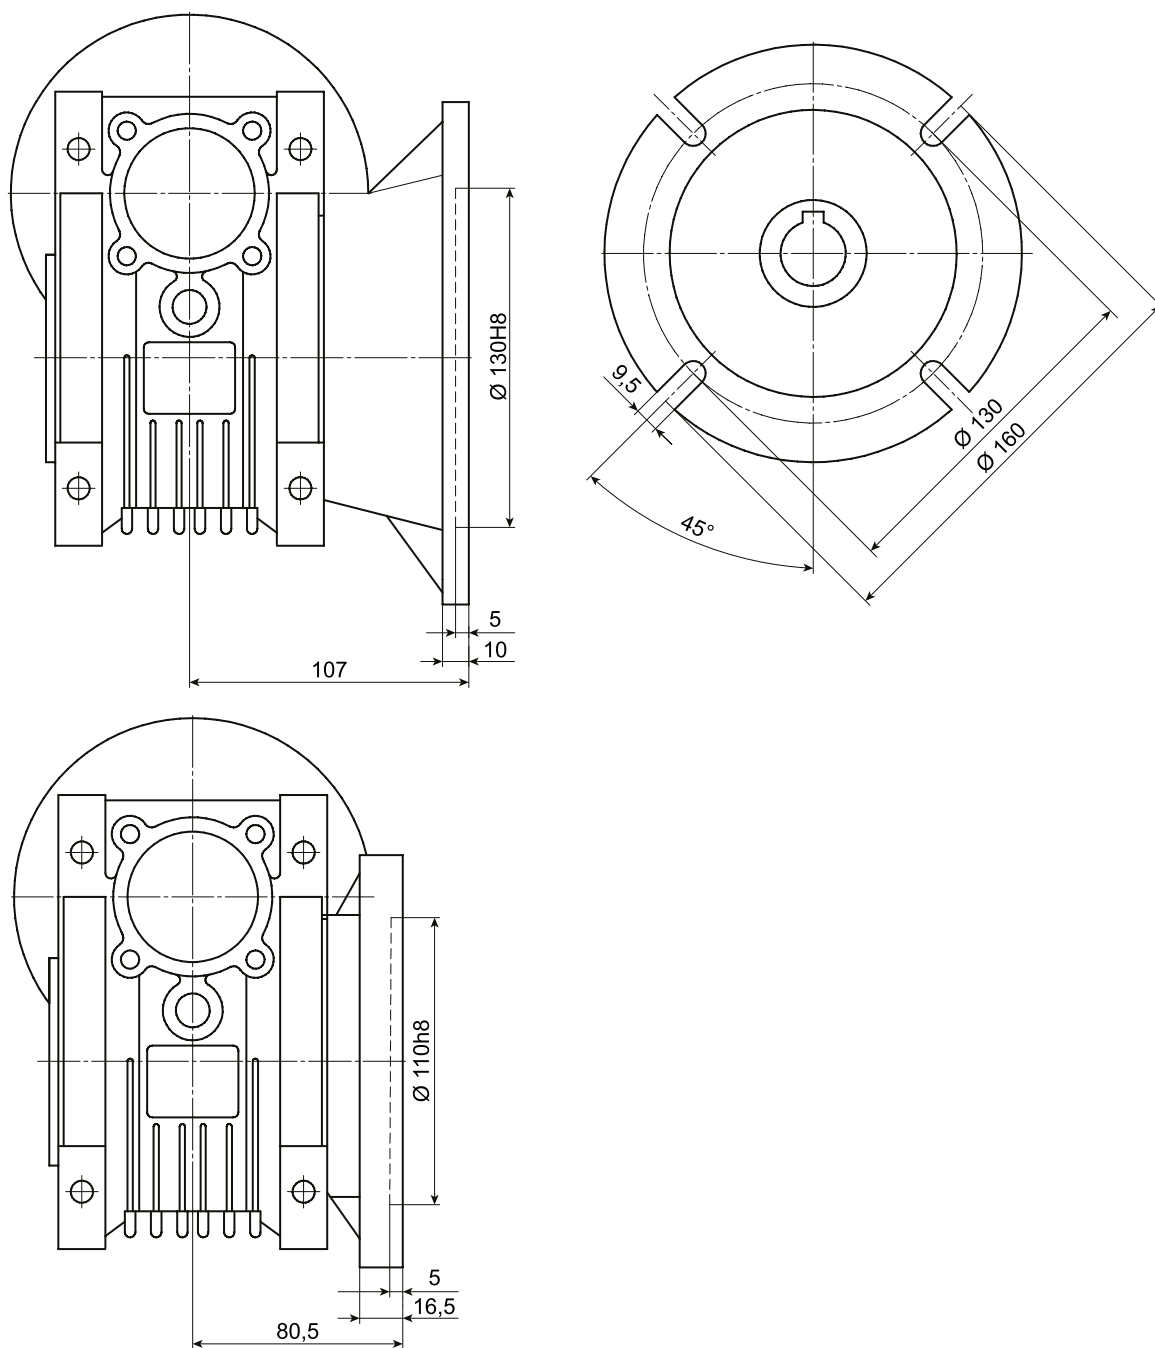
Габаритные размеры боковых фланцев FC и FD
